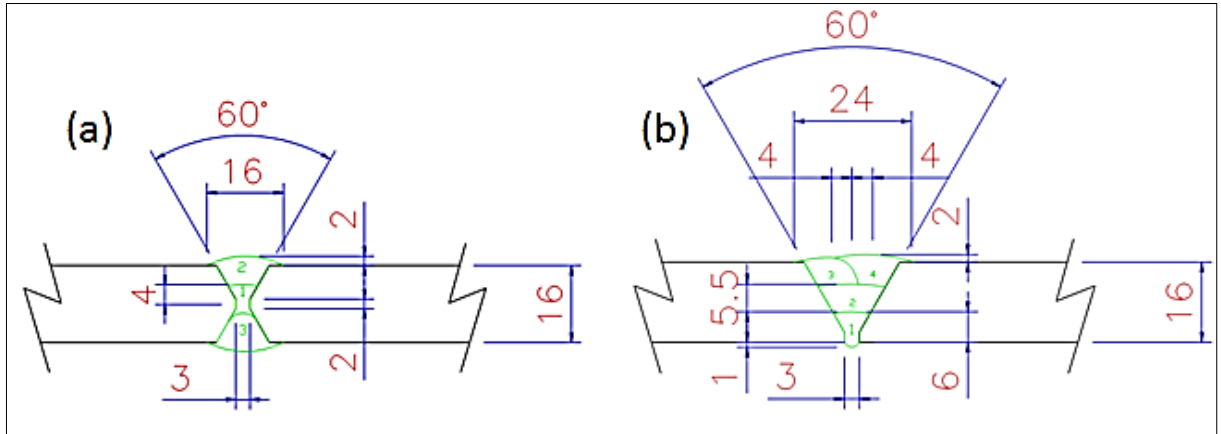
Sequência de soldagem dos cordões de solda nas juntas em “X” e “V”.
